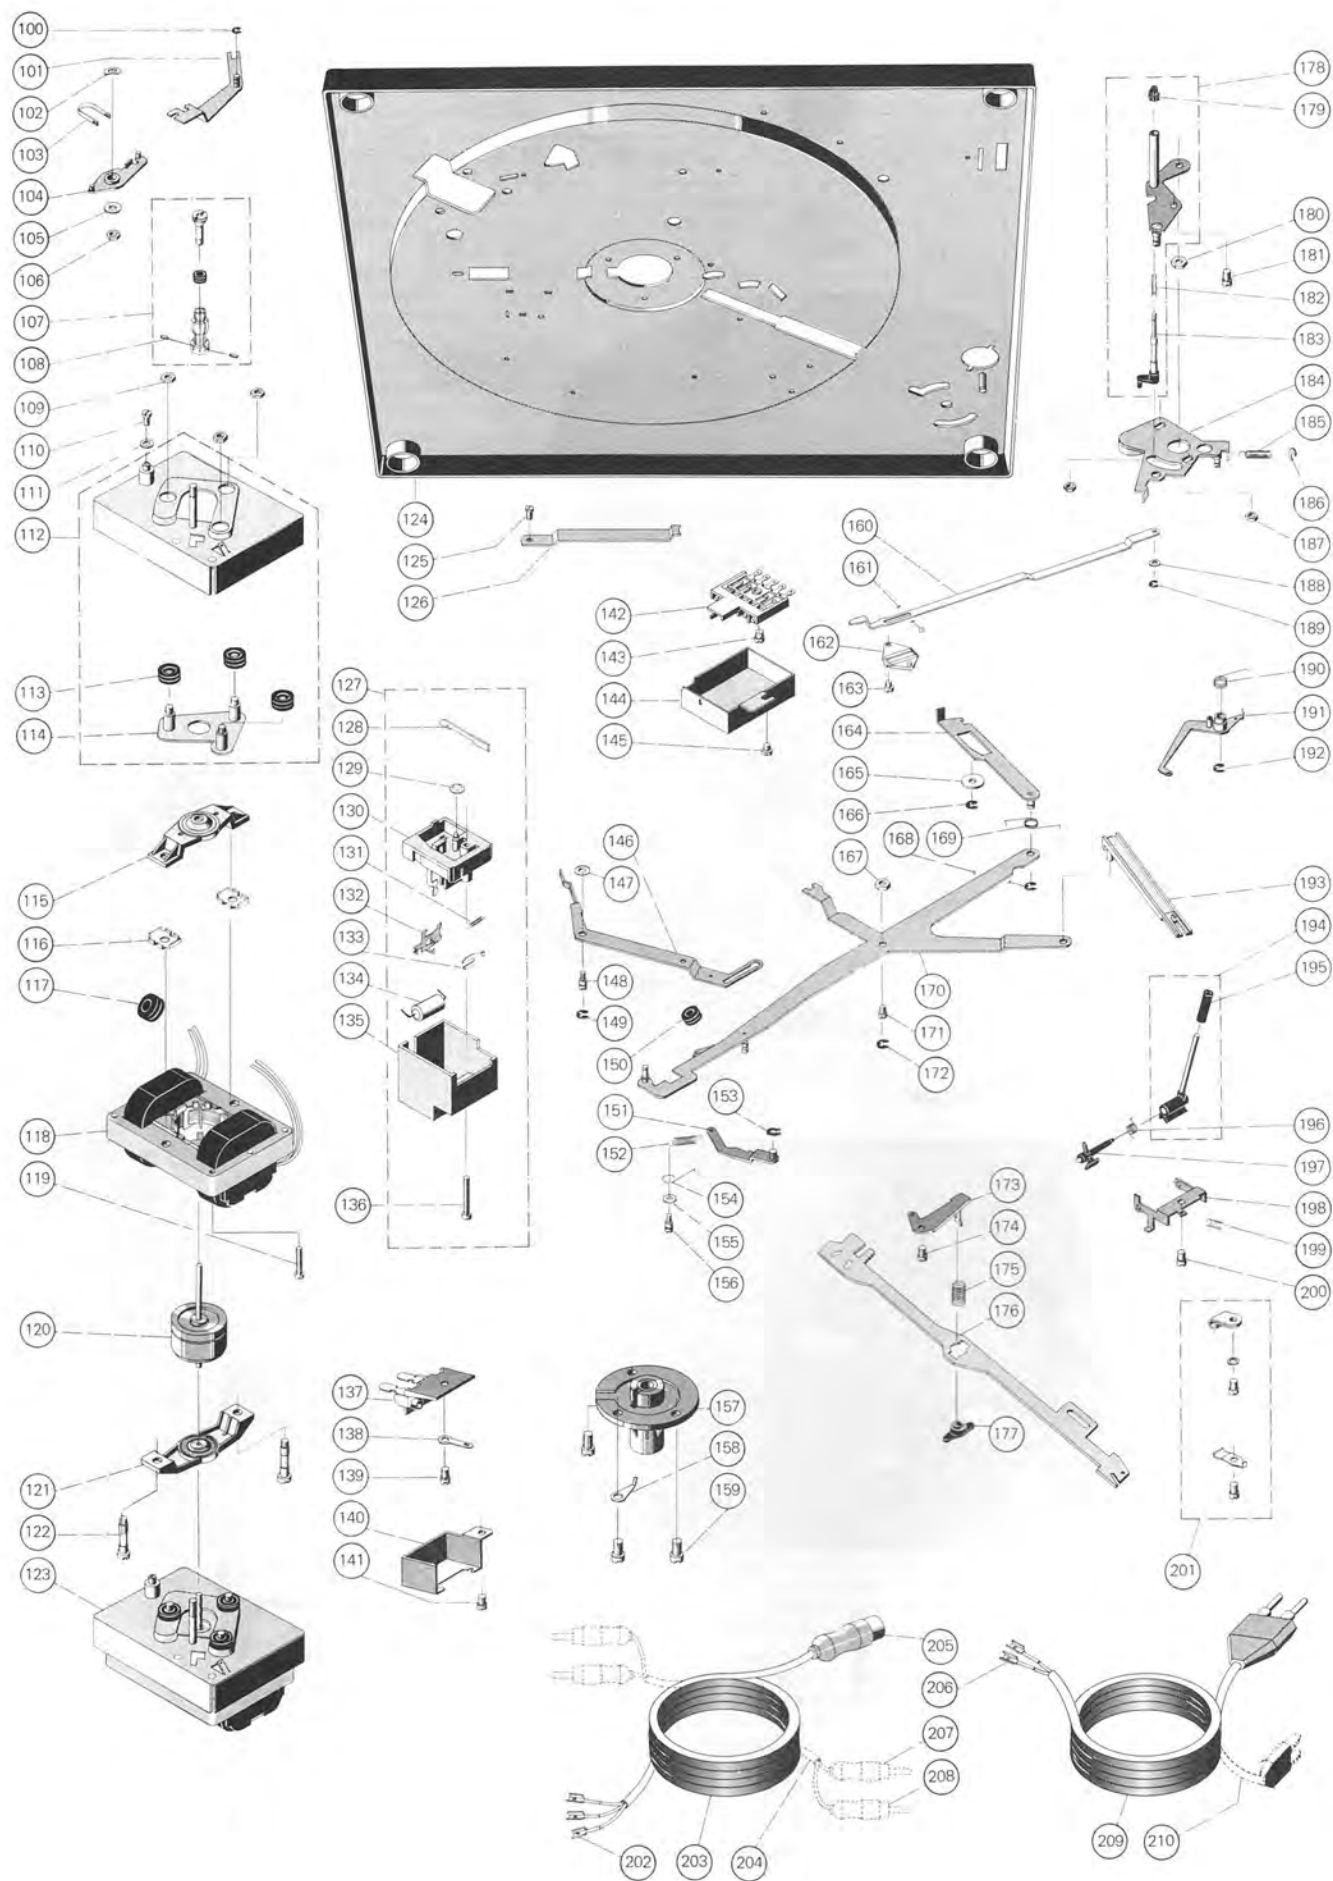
Explosionszeichnung Teile unter der Einbauplatte
